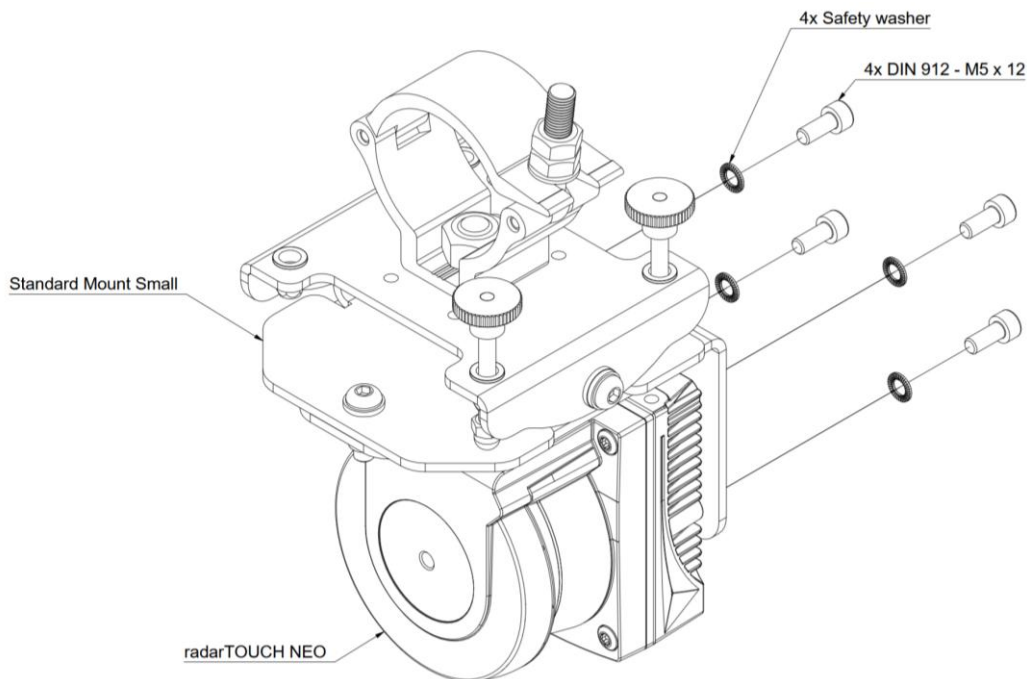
Explosionszeichnung Montage an Standard Mount Small
